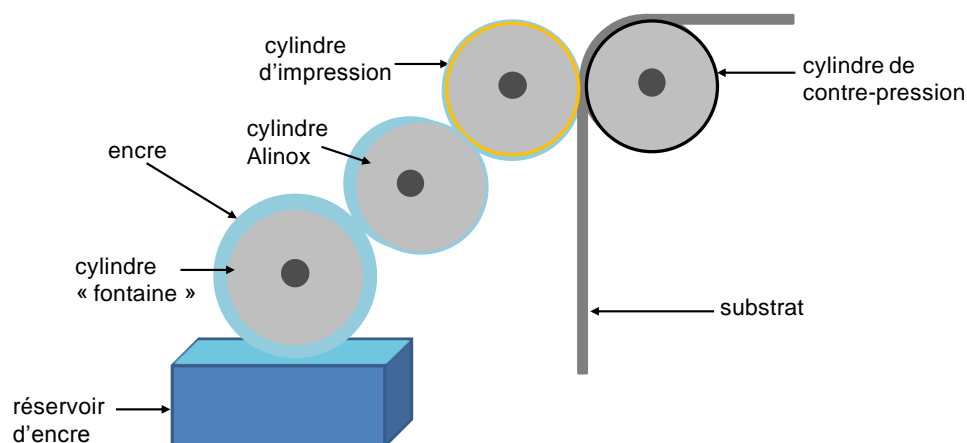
Ligne de fabrication d'un procédé roll to roll
